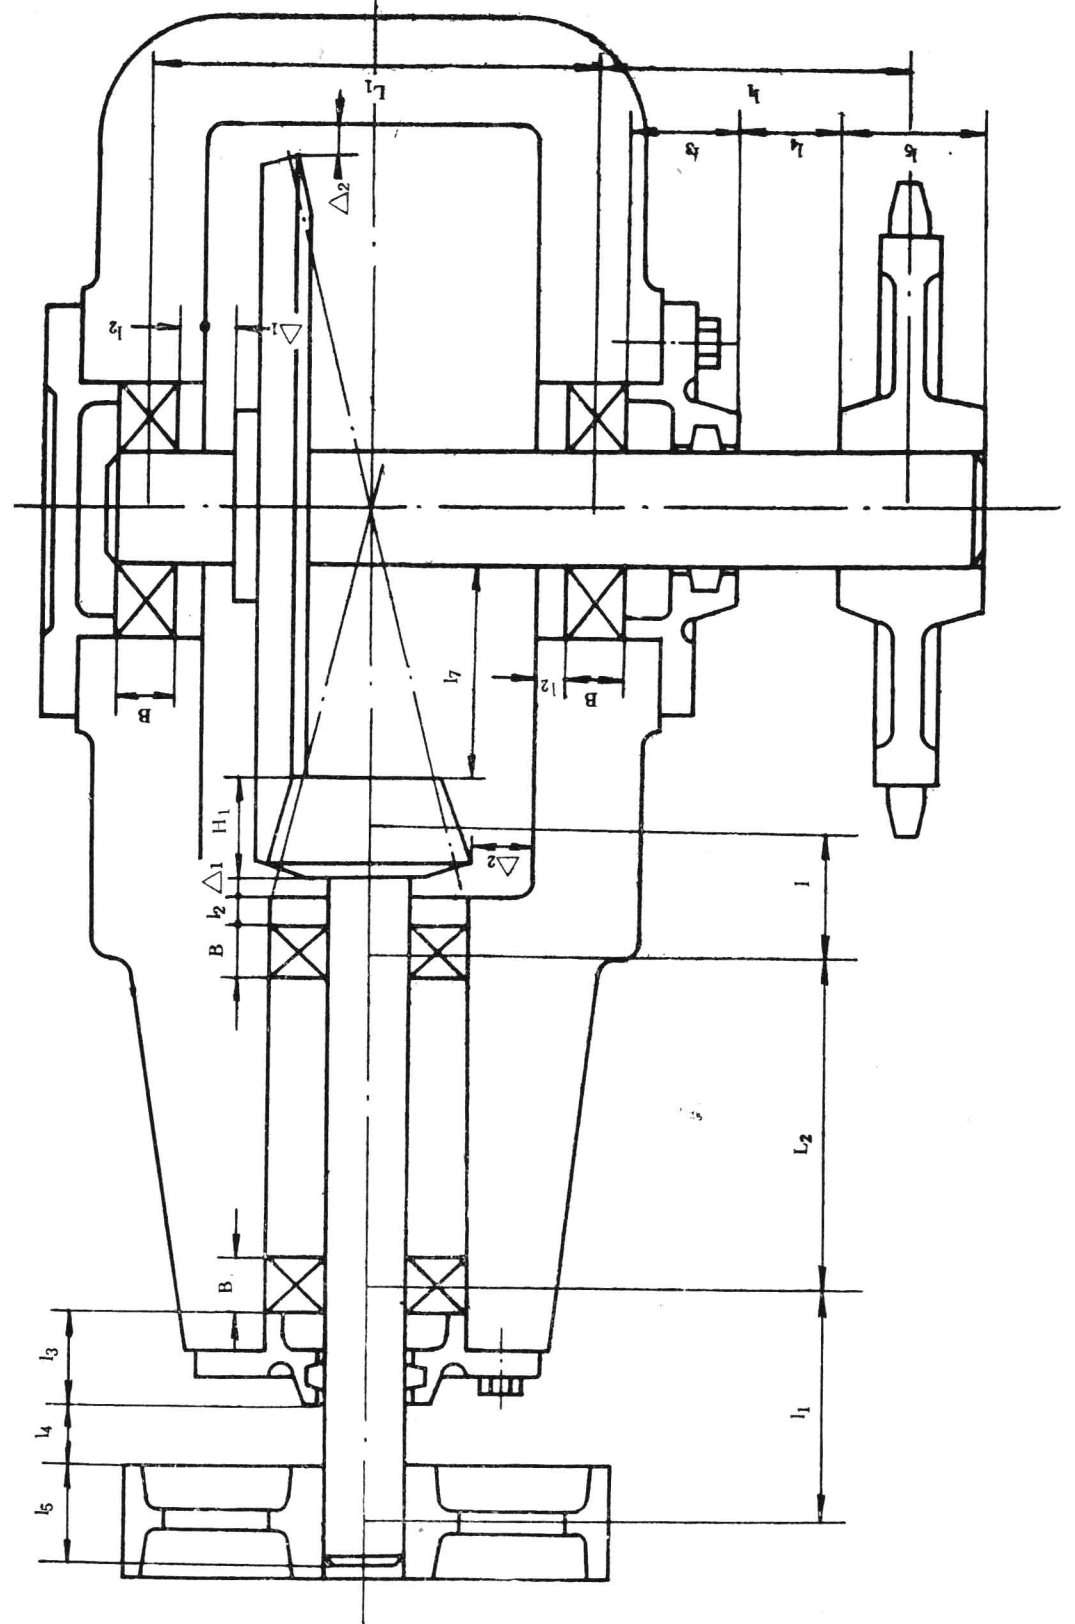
单级圆锥齿轮减速器零件的位置尺寸
